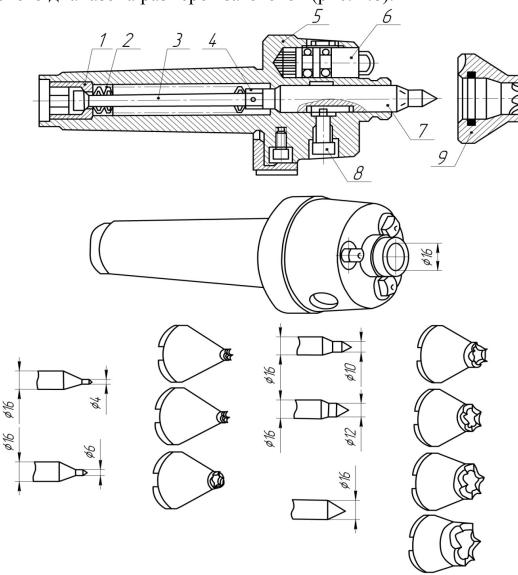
Поводковый зубчатый патрон со сменным центром и поводками: 1, 4 — гайки; 2 — пружина; 3, 8 — винты; 5 — корпус; 6 — поводок; 7 — сменный плавающий центр; 9 — сменный поводок
